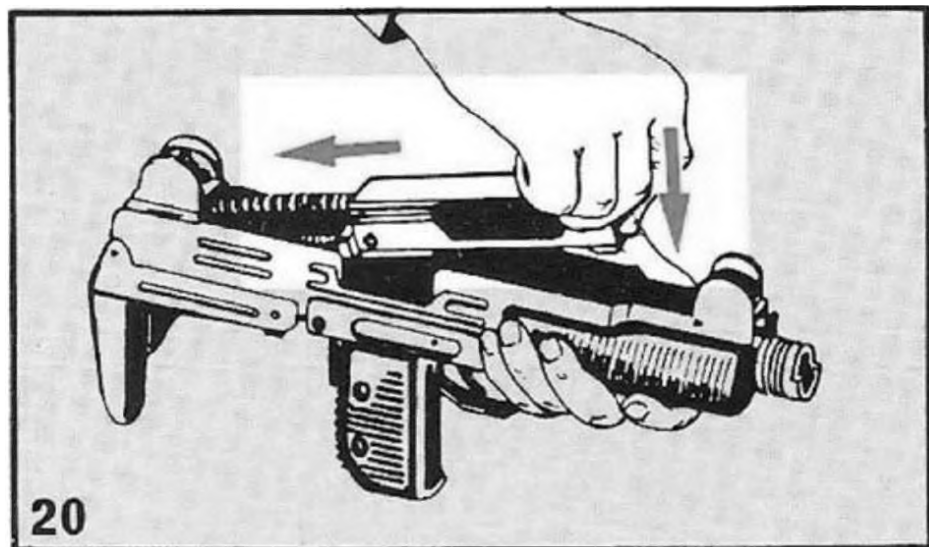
Порядок вилучення затвора і зворотньої пружини
